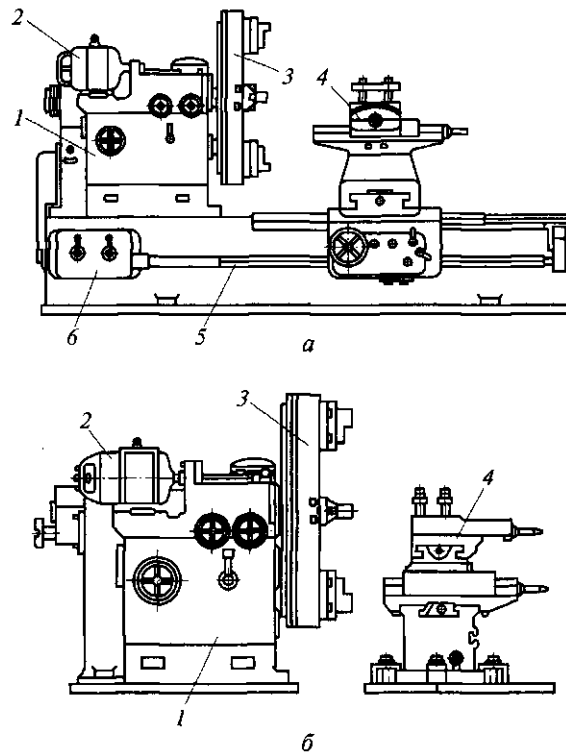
Лоботокарные станки с единой (а) и раздельной (б) станиной: 1 — коробка скоростей; 2 — главный электродвигатель; 3 — планшайба; 4 — суппорт; 5 — ходовой вал; 6 — коробка подач
